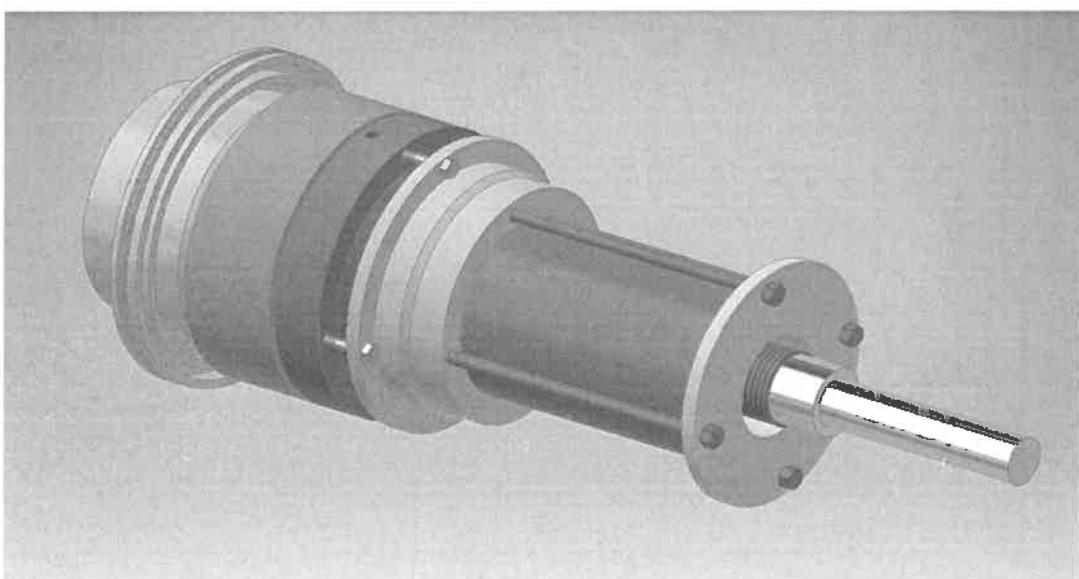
Устройство для демонтажа внутренних колец буксовых подшипников
